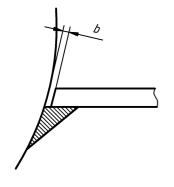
Préparation et ajustage des bords à souder — Soudures bout à bout dans des assemblages entretoise-membrure à profils creux circulaires
